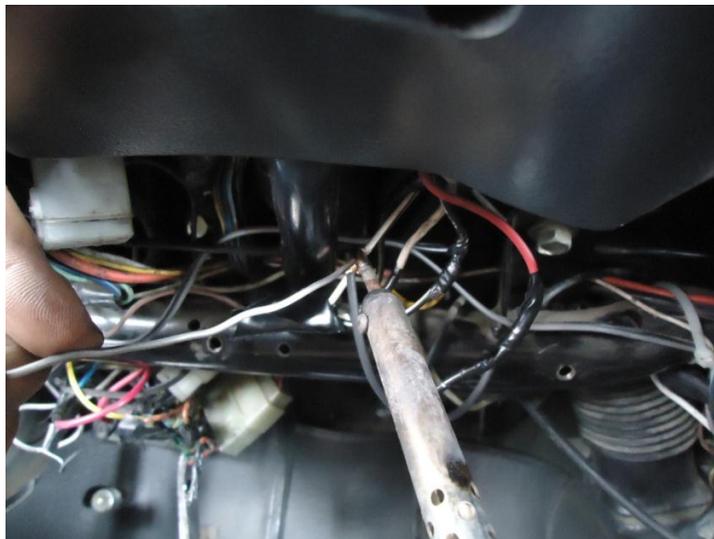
Soldadura con caudín y estaño de cables.
